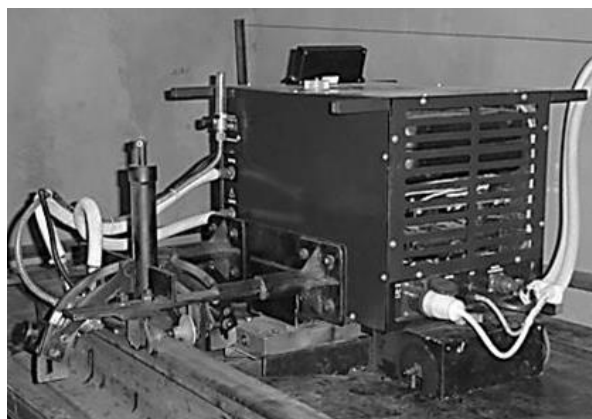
Установка для плазменного упрочнения боковой поверхности головки рельса верхнего строения пути
